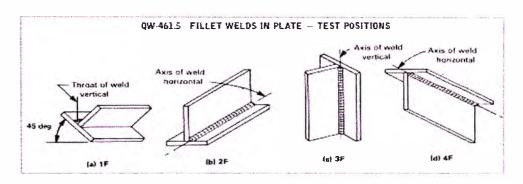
posiciones de prueba en planchas – Juntas de Filete
